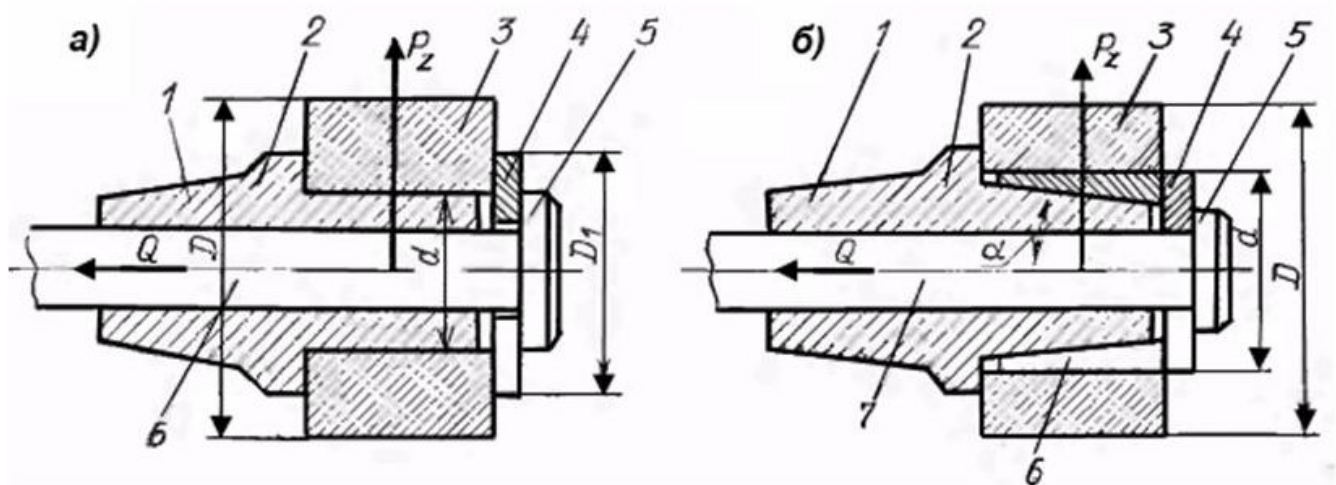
Конструкції оправок: а- гладка оправка б – Оправка з розрізаною втулкою
